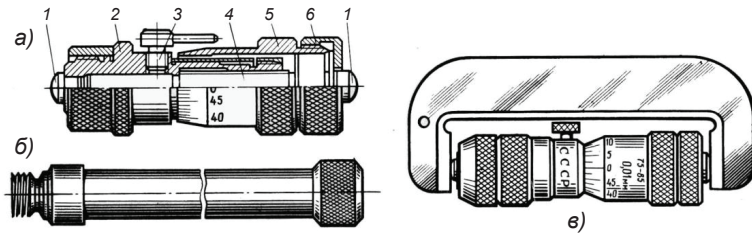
Микрометрический нутромер (штихмасс): а) устройство; б) удлинительный стержень; в) проверка нулевого положения; 1 – измерительные поверхности, 2 – стебель, 3 – стопор, 4 – микрометрический винт, 5 – барабан, 6 – гайка
